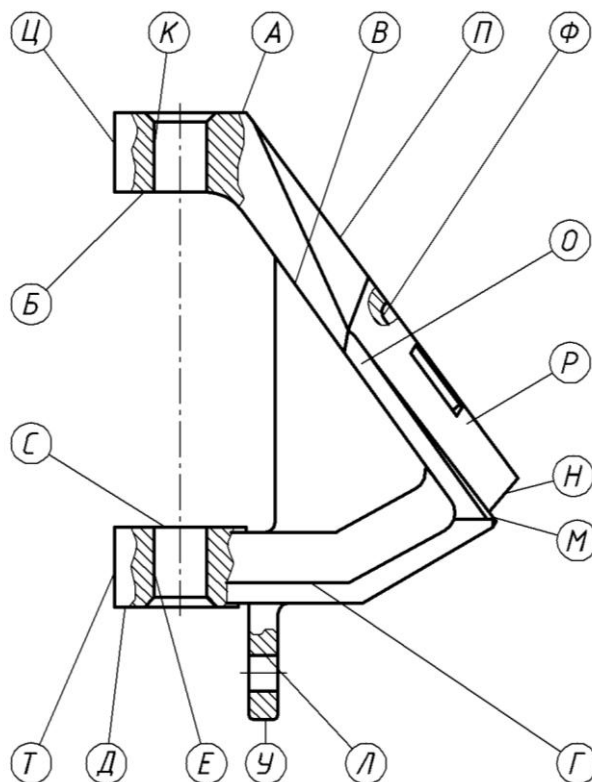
Загальний вигляд деталі з позначеними поверхнями
